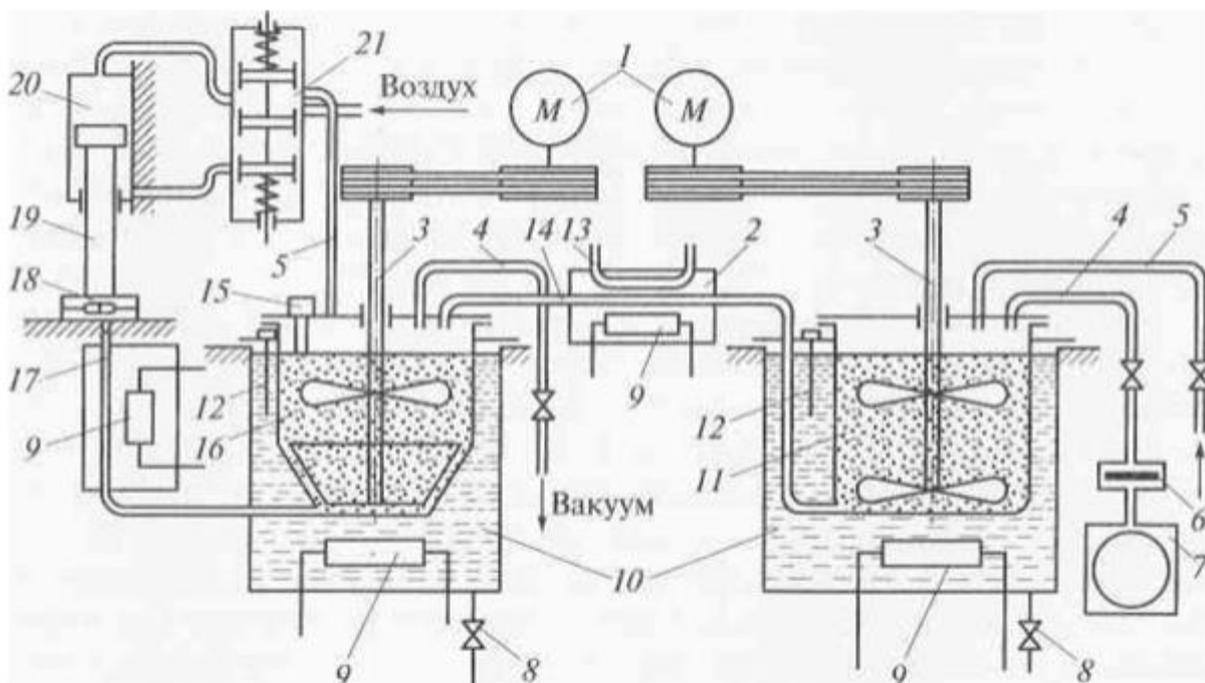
Схема литейного полуавтомата: 1 — электродвигатели; 2 — дросселирующее устройство; 3 — мешалка; 4 — вакуумпровод; 5 — трубопровод сжатого воздуха; 6 — ловушка; 7 — механический вакуумный насос; 8 — сливной вентиль; 9 — нагреватель; 10 — глицерин; 11, 16 — вспомогательный и рабочий шликерные баки; 12, 15 — датчики
